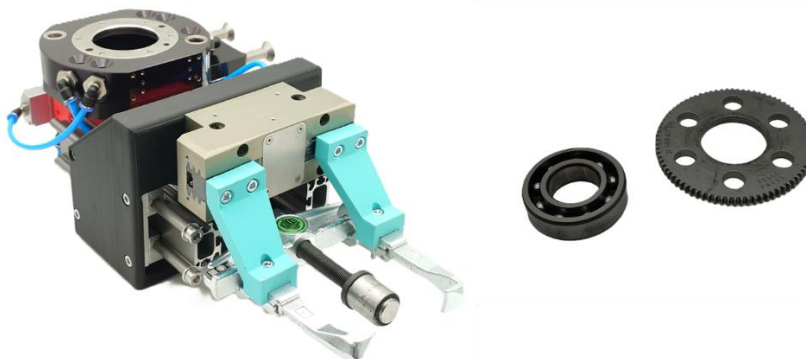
Abziehwerkzeug (links), Lager und Drehzahlgeberrad (rechts)
